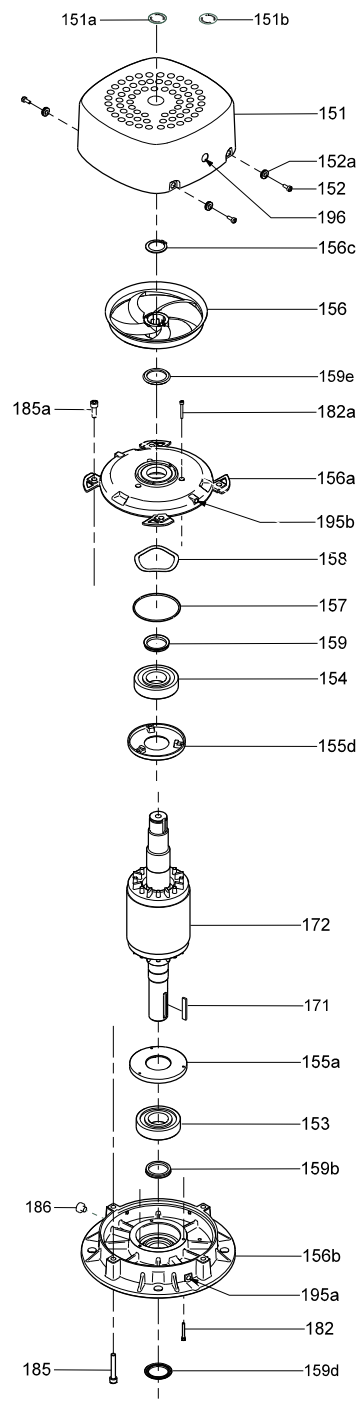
Детализовка на рис. 78 электродвигателя MGE-F в разобранном виде.
